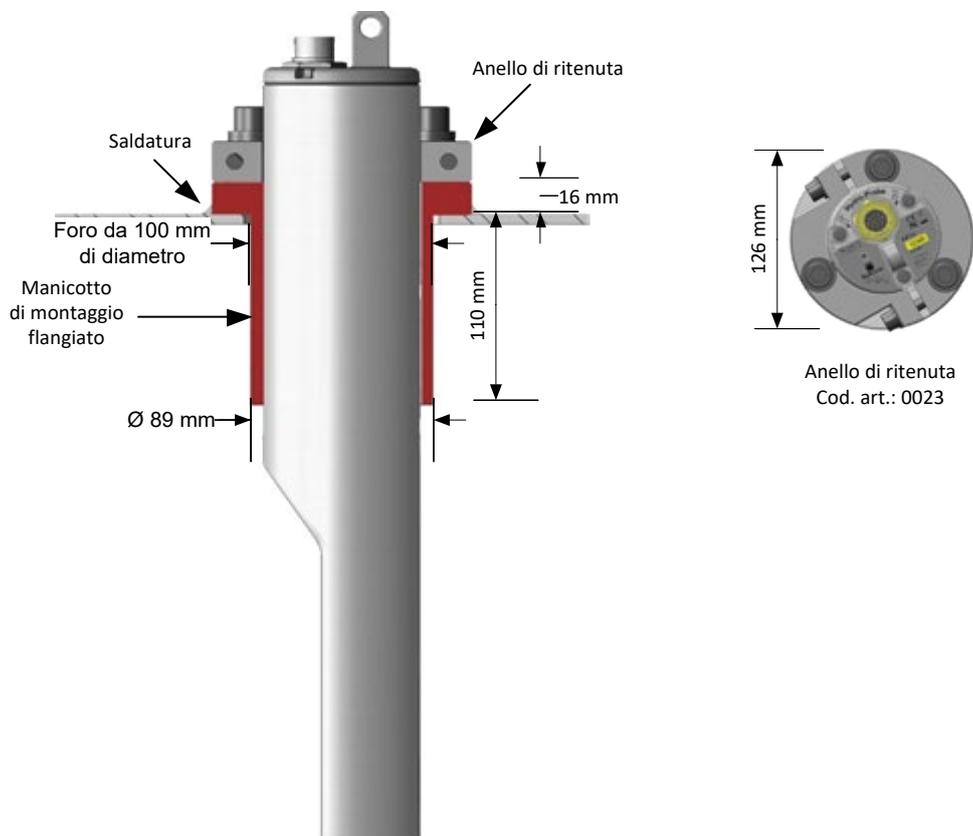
Manicotto di montaggio flangiato (cod. art. 0024A)
